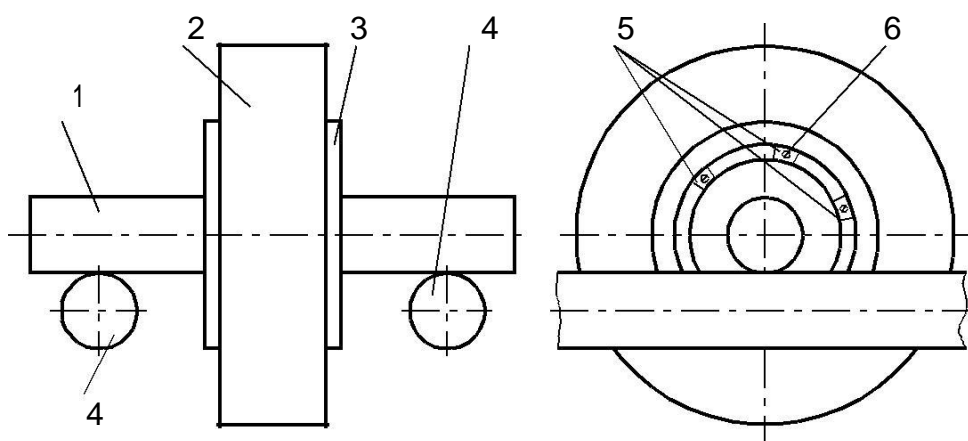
Схема статической балансировки шлифовального круга на станке с цилиндрическими направляющими: 1 - оправка; 2 - шлифовальный круг; 3 - планшайба; 4 - направляющие; 5 - уравнивающие грузы; 6 - крепежные элементы
